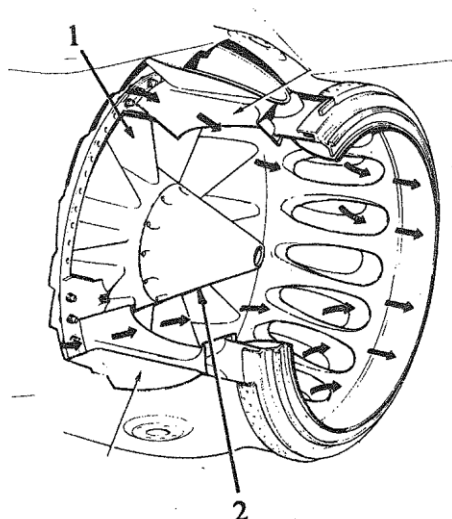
[53] Výstupní soustava proudového motoru;
